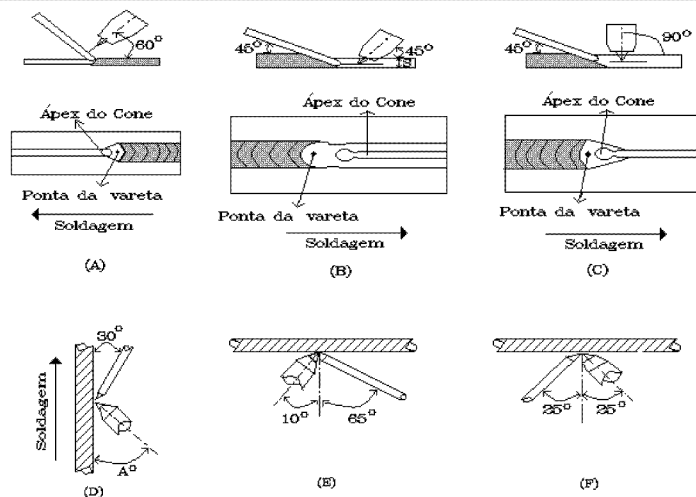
Métodos de Soldagem por Oxi-Gás.
